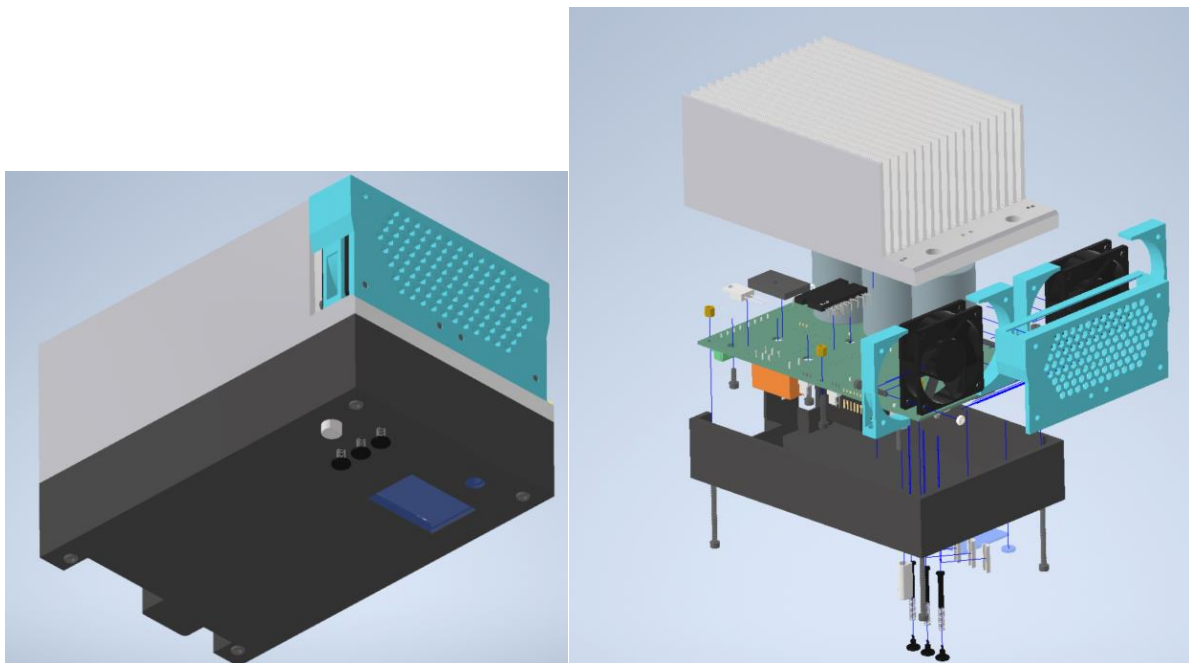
Montiertes Gehäuse, links und Explosionszeichnung rechts
